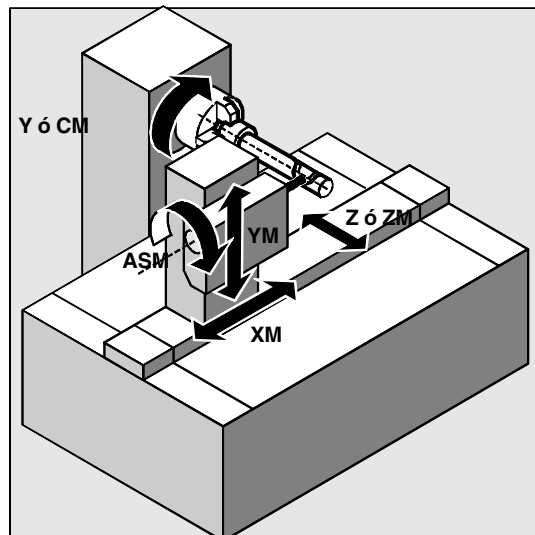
Cinemática de máquina especial con eje de máquina Y (YM) adicional
